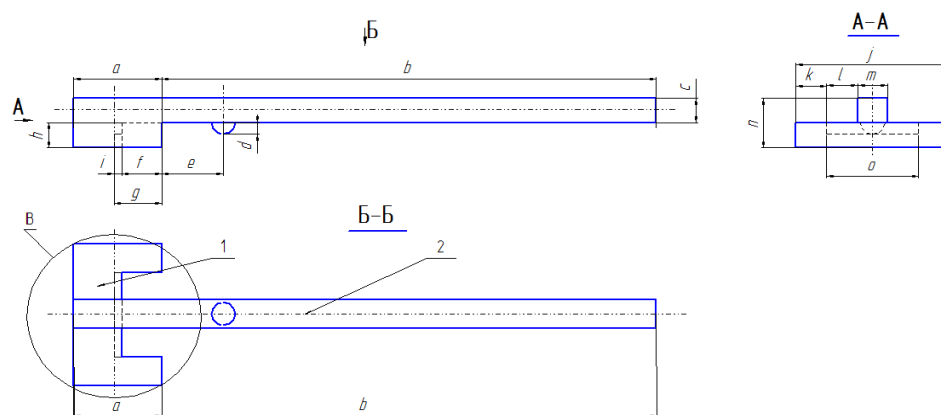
Конструкція колійного пристрою по вимірюванню пружних властивостей клеми КПП-5 проміжного рейкового скріплення типу КПП-5:
